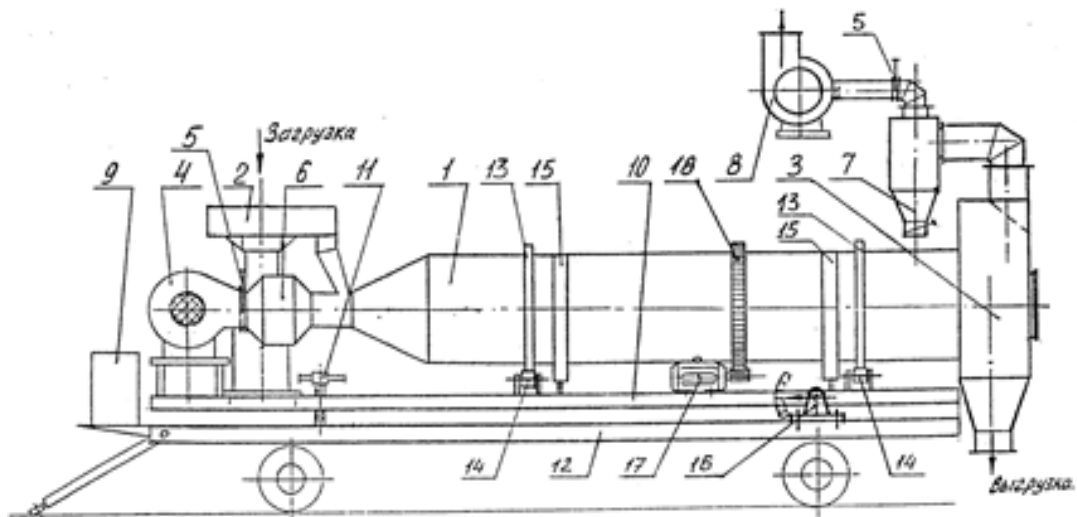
Схема передвижного сушильно-охладительного агрегата для термообработки поваренной соли [6]
